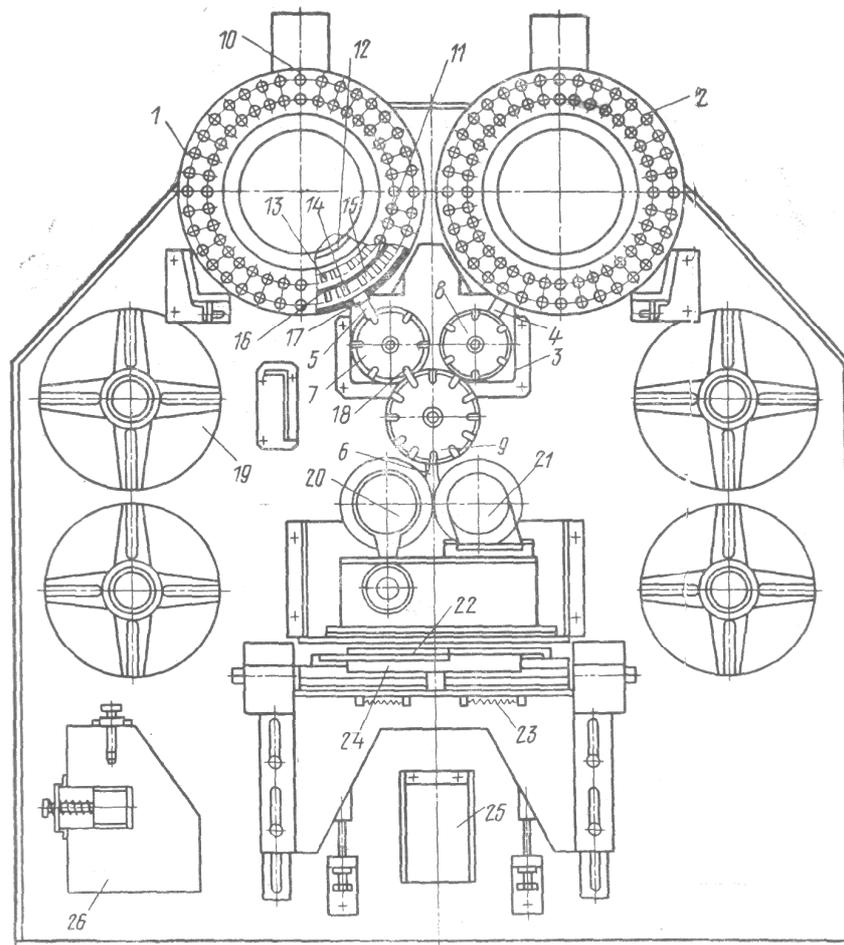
Устройство для упаковки цилиндрических изделий (вид спереди)
